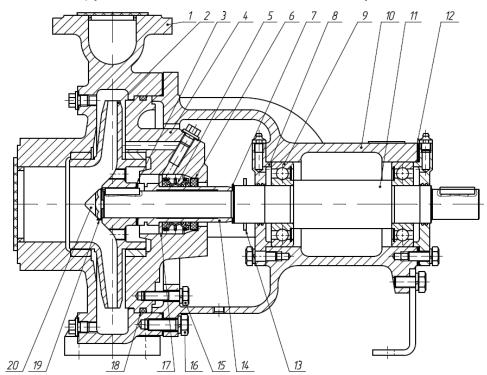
Конструкция насоса К с торцевым уплотнением вала: 1 — напорный патрубок; 2 — рабочее колесо; 3 — шпонка; 4 — корпус; 5 — уплотняющая жидкость; 6 — торцевое уплотнение вала; 7 — упорная шайба; 8 — крышка подшипника; 9 — подшипник качения; 10 — корпус подшипниковой камеры; 11 — вал; 12 — прокладка; 13 — упорное кольцо; 14 — втулка вала; 15, 16 — крепежно-регулировочные болты; 17 — упорное кольцо; 18 — уплотнение; 19 — крепление рабочего колеса; 20 — головка крепления
